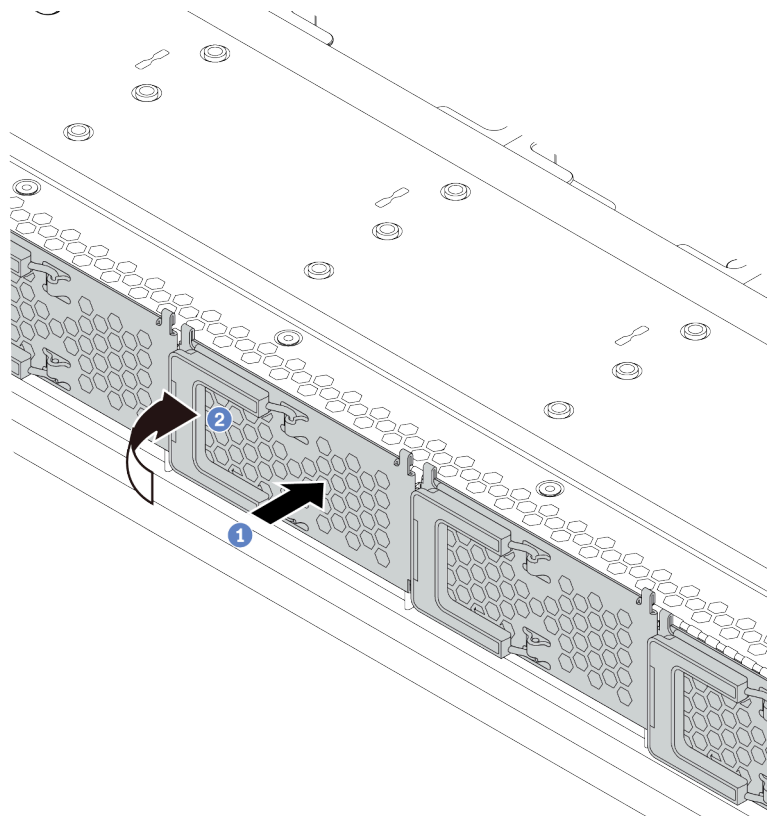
Installation du couvercle du boîtier d'unités de disque dur EDSFF
